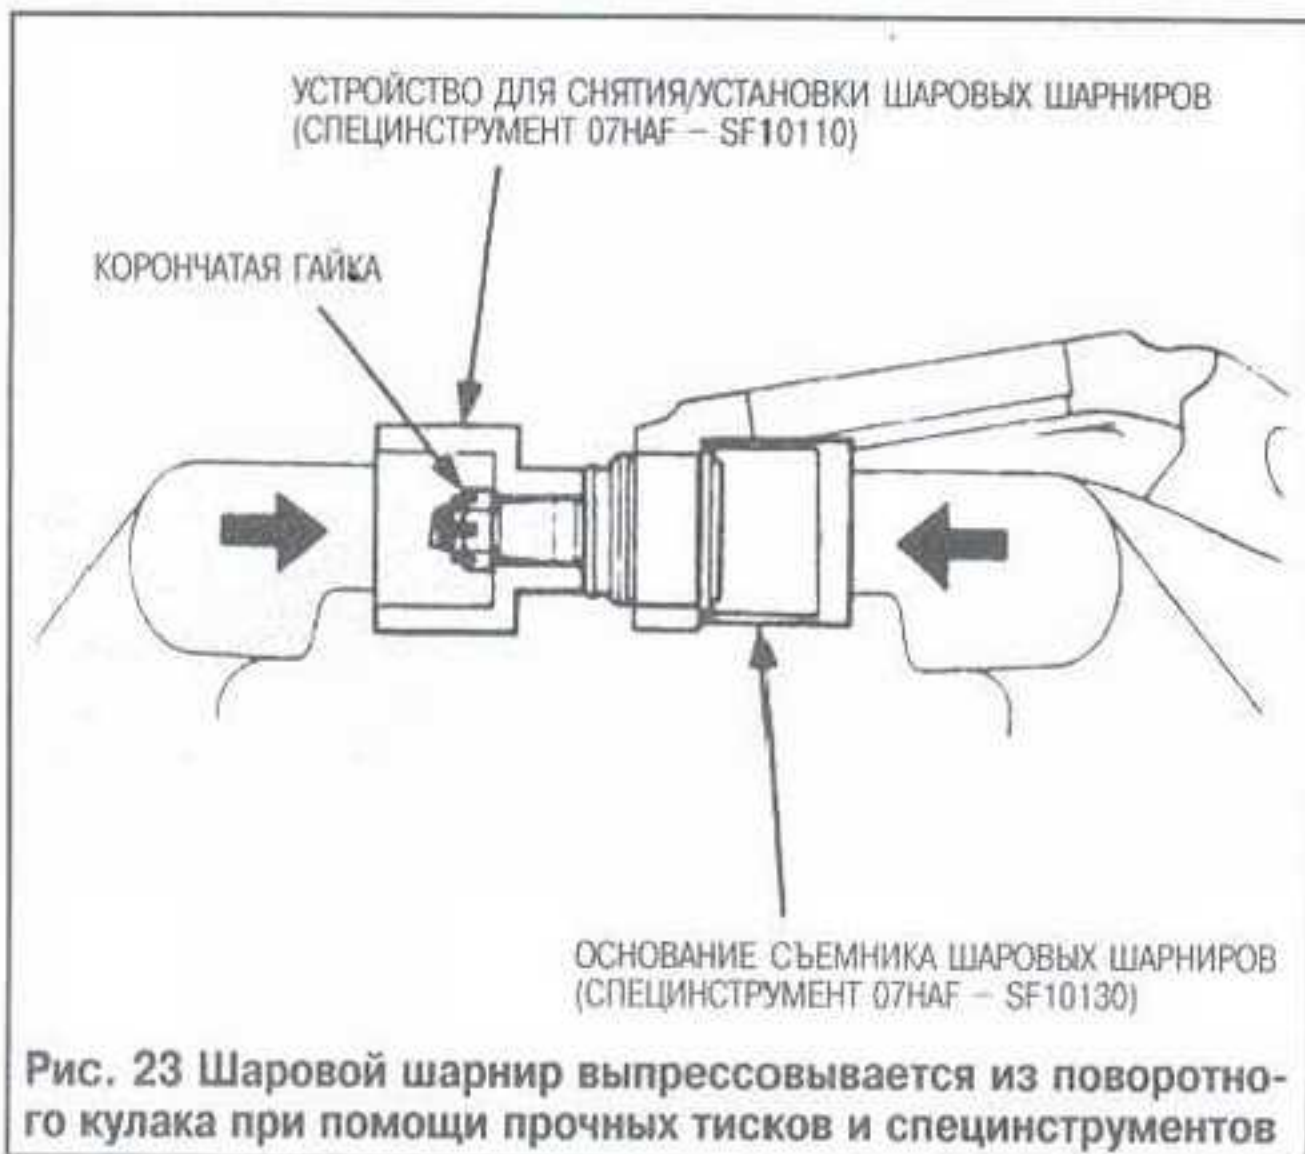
Шаровой шарнир выпрессовывается из поворотного кулака при помощи прочных тисков и специнструментов
